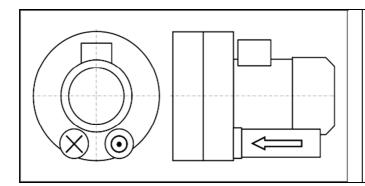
Двухпоточная конструкция вакуумного насоса/компрессора с двумя рабочими колесами.
